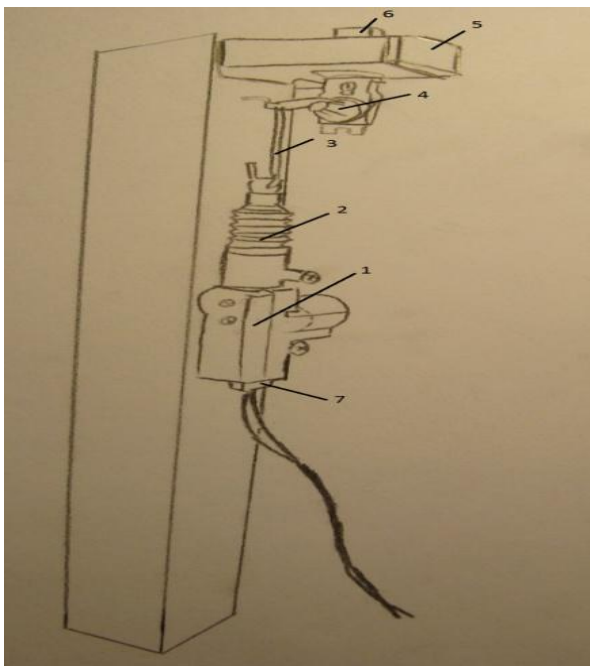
Блок расчеховки дополнительного устройства для активации качающейся мишени «Свингер»: 1 – корпус; 2 – расчеховочное устройство; 3 – чека; 4 – переходник; 5 – балка крепления; 6 – подвижный язычок; 7 – разъем для подключения внешнего устройства
